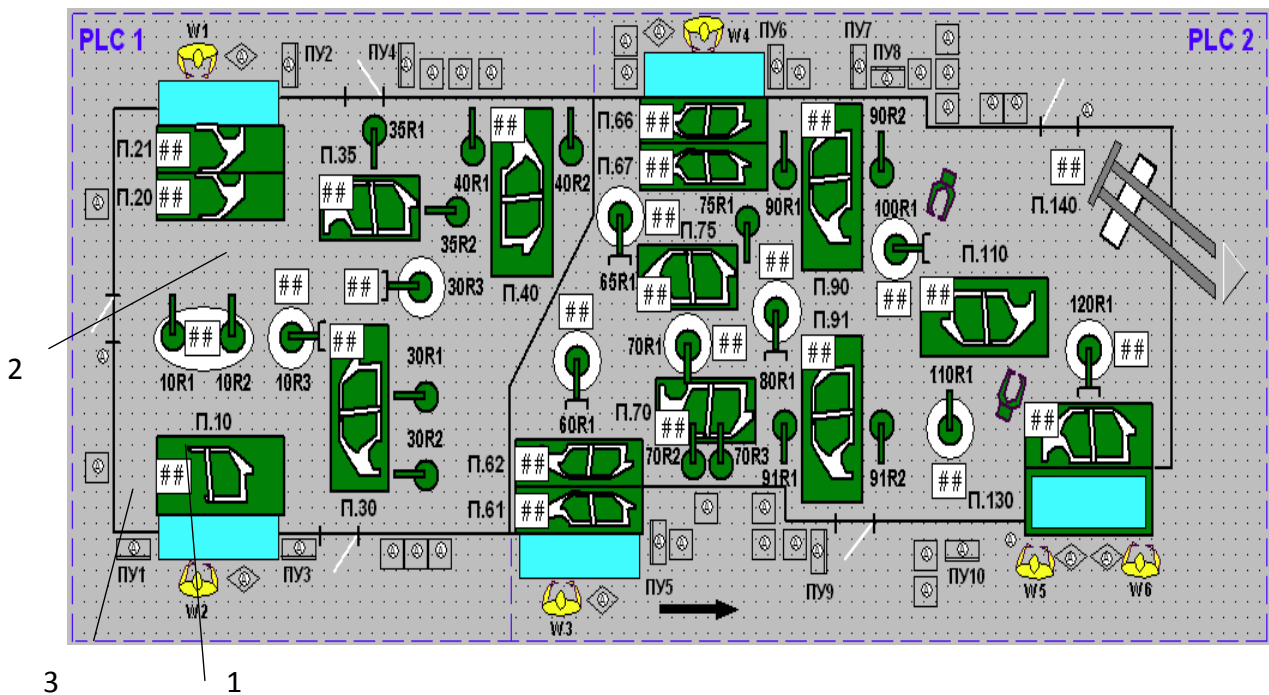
Автоматизированная линия сварки боковин автомобиля
